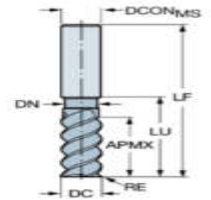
кінцева фреза R216.24-20050FCC44P 1620
